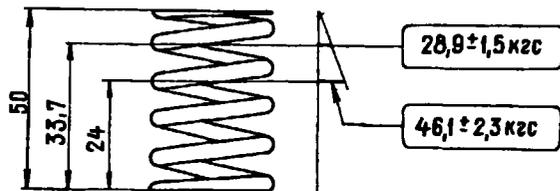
Основные данные для проверки наружной пружины клапана
